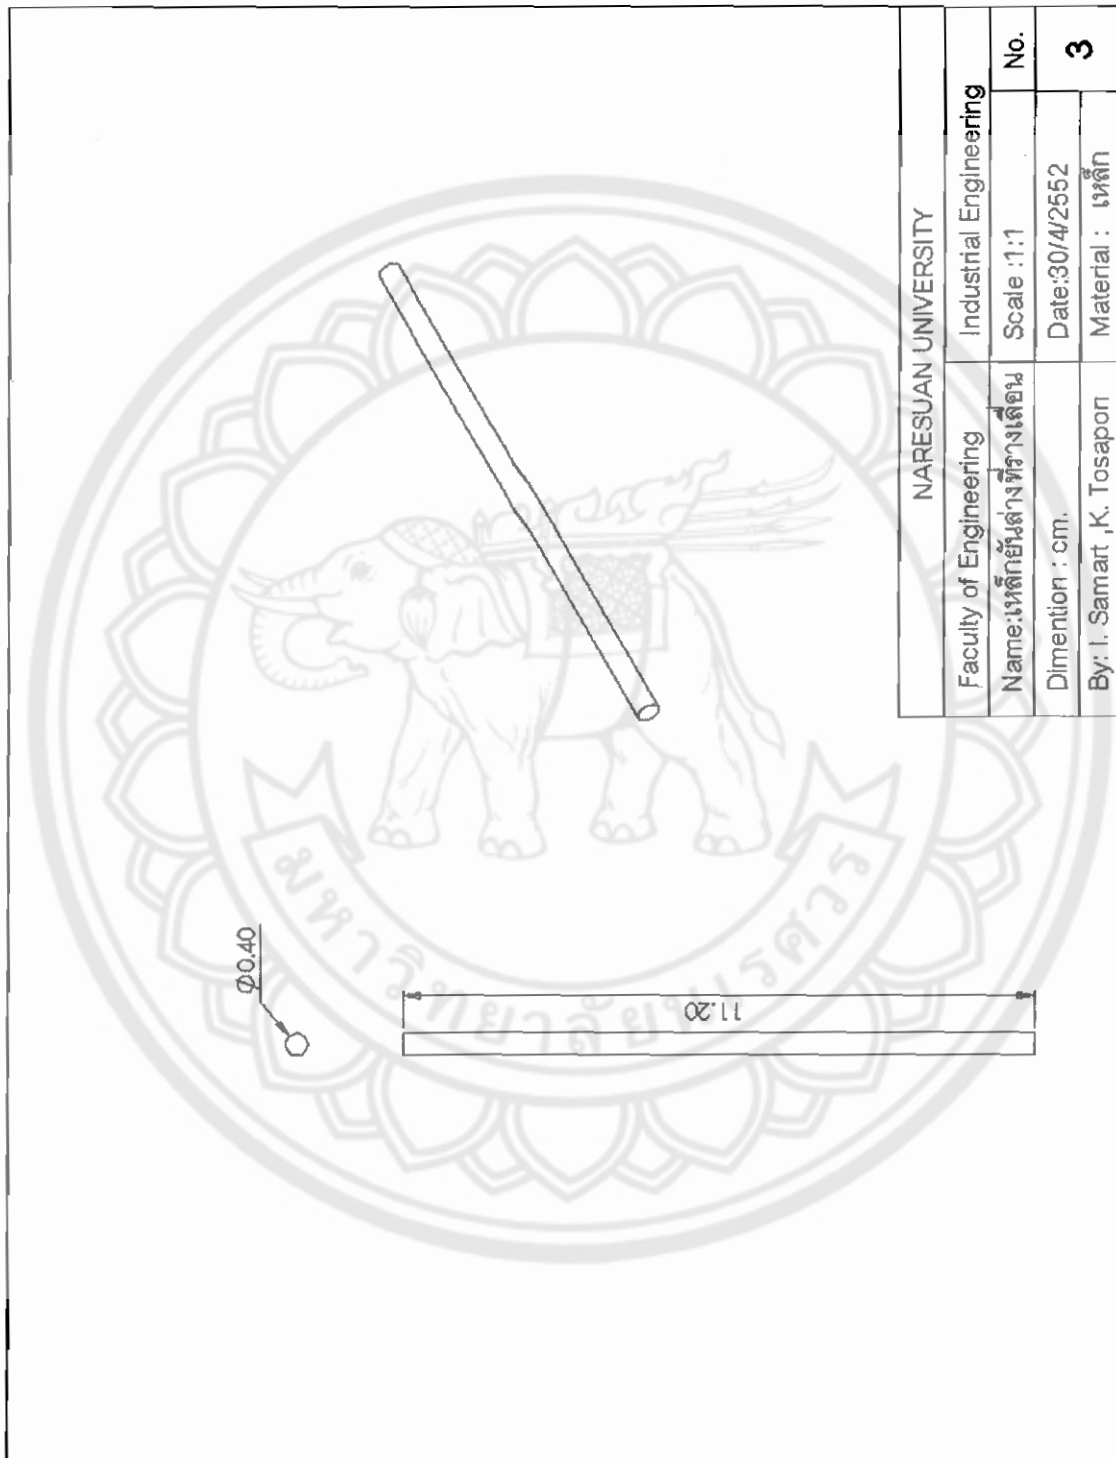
แสดง Assembly Drawing ตัวยึ่นรางเลื่อน
